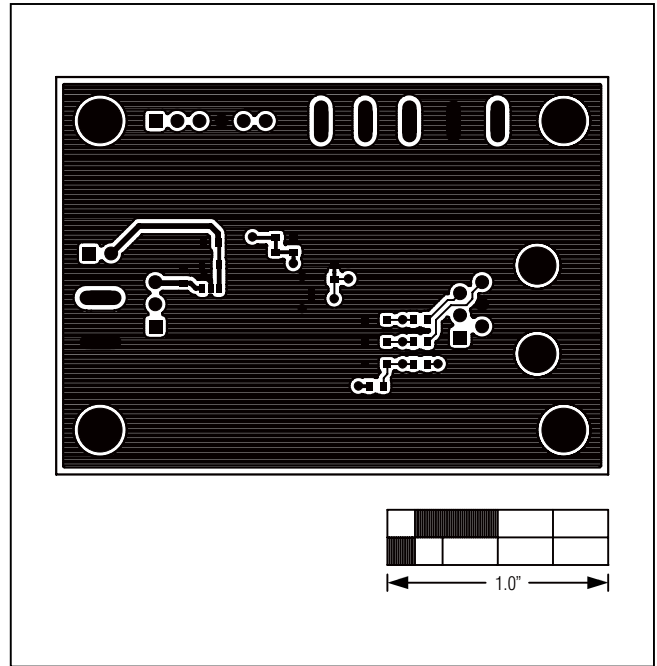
MAX17058/MAX17059评估板PCB布局——焊接层
